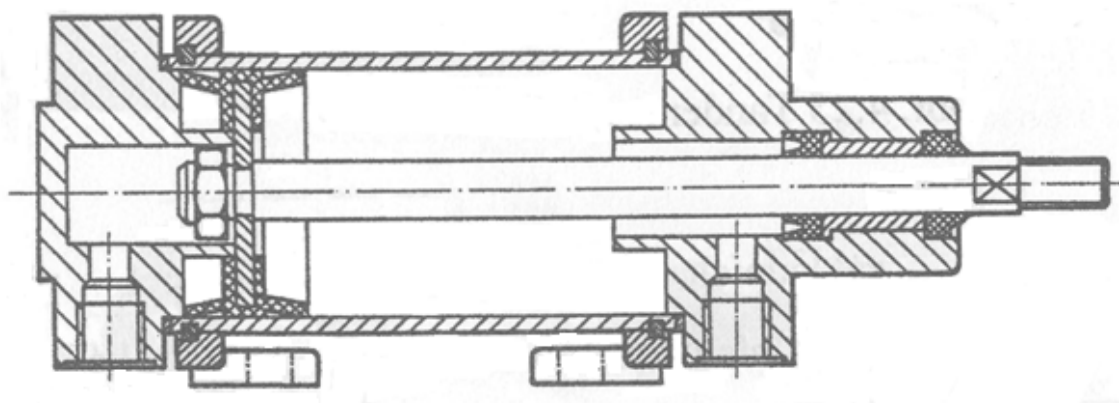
Konstrukce pneumatických přímočarých motorů
